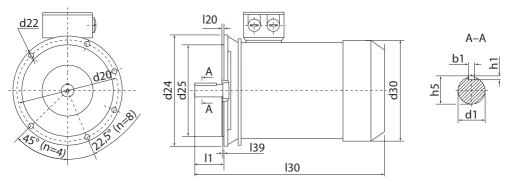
Габаритные и установочные размеры (исполнение 3081)
